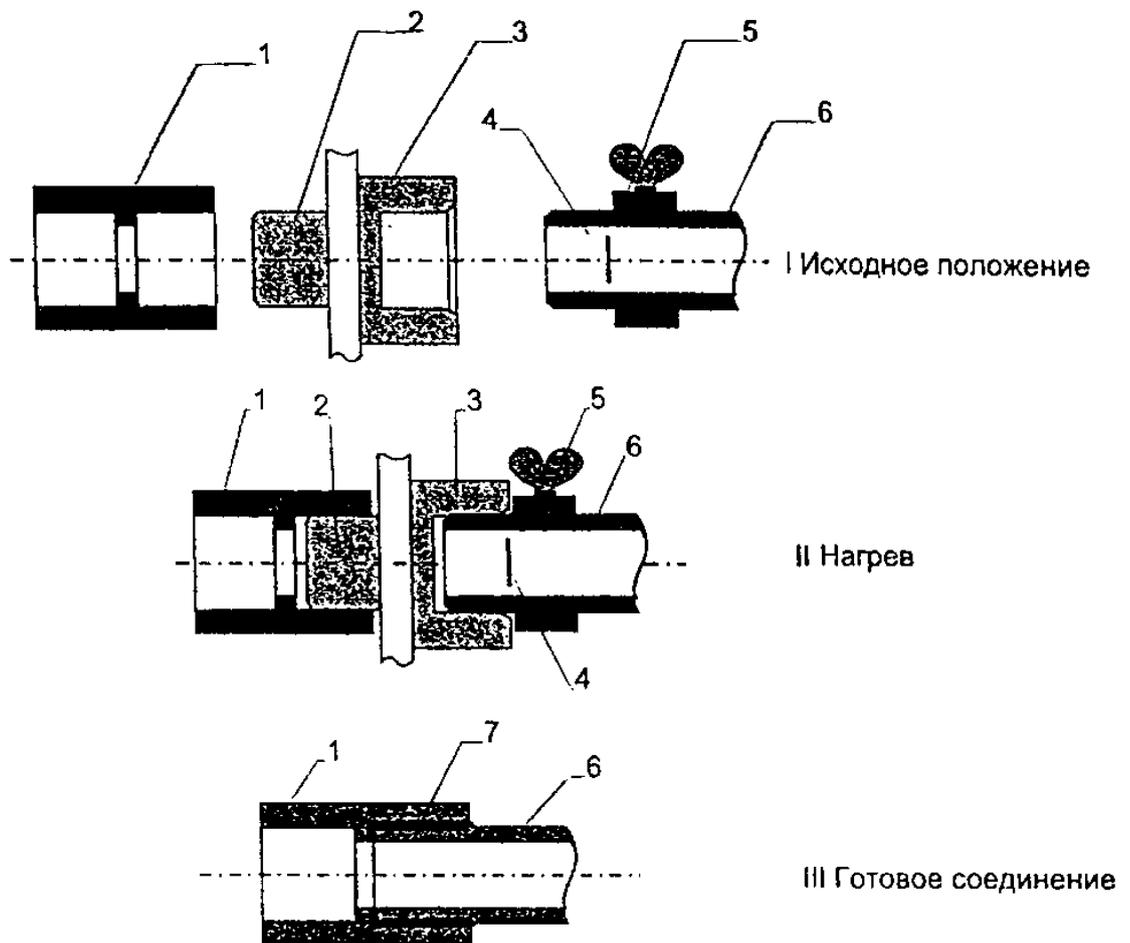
Последовательность процесса контактной сварки труб и муфты из PPRC
